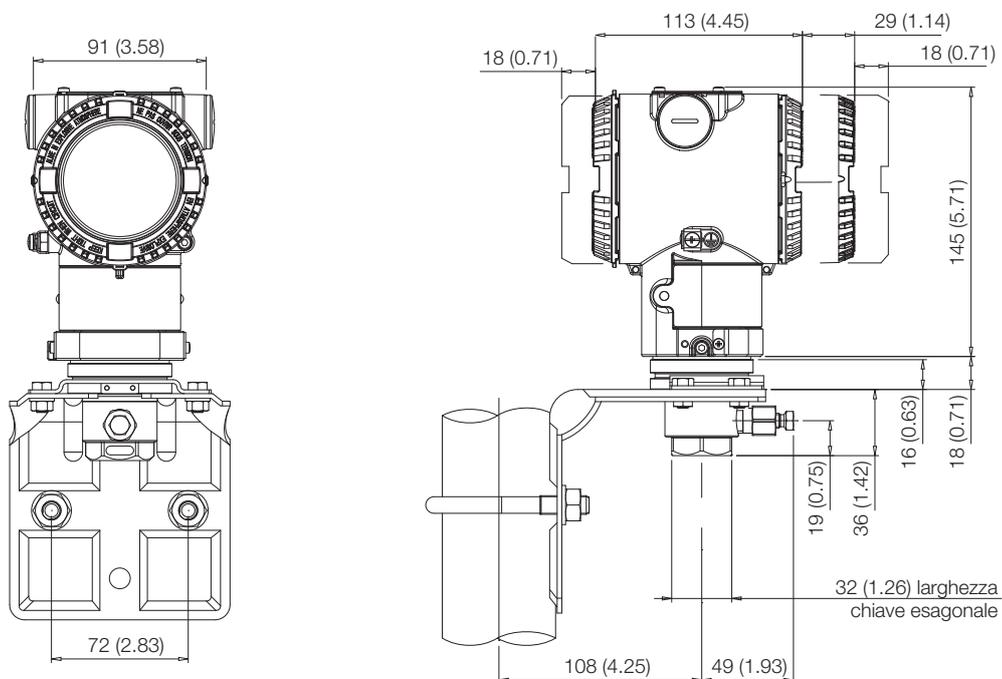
Trasmettitori P-Style modello 266H o 266N a elevata sovrappressione con connessione di processo 1/2-14 NPT femmina e barileto dell'housing installati su palina da 2 pollici tramite kit staffa (rispettivamente B6 in acciaio al carbonio e B7 acciaio inossidabile 316L)
